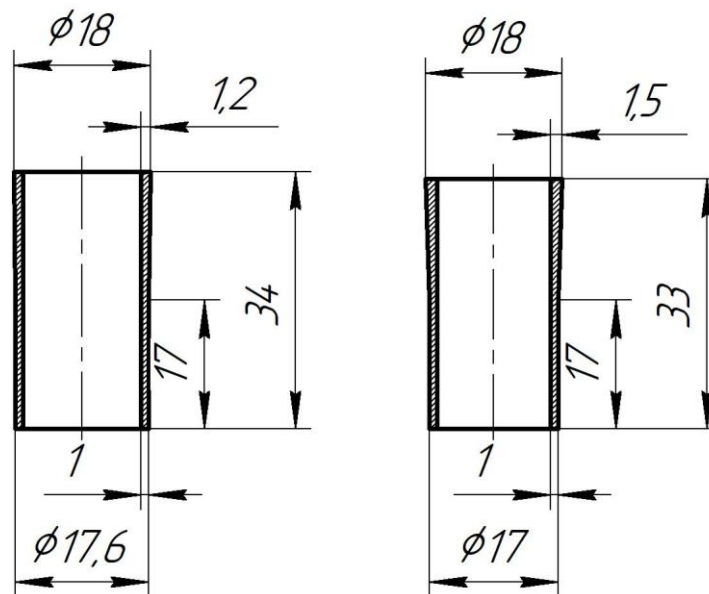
Попередньо прийняті трубчасті заготовки змінної товщини для виготовлення кумулятивної воронки
